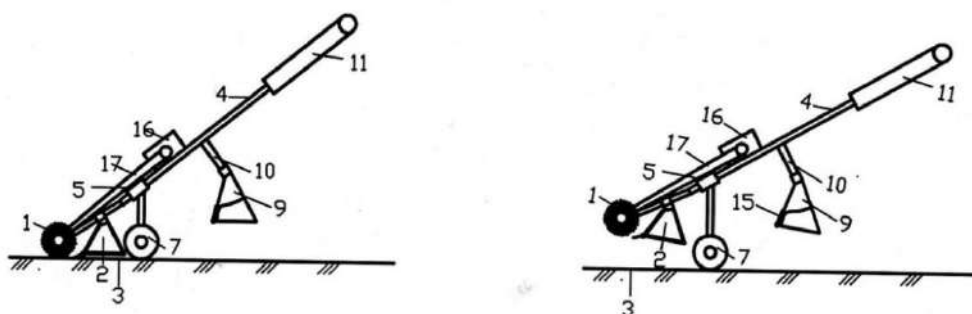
Рычажное барабанное устройство для подметания улиц и дорог: 1–барабанная щетка; 2 – призматический савок; 3– дорога ; 4 – черенок; 5 – патрубок; 6 – ось ОПМ; 7 – колеса; 8 – рама; 9 – компенсирующий призматический савок; 10 – кронштейн; 11 – рукоятка; 12 – винт; 13 – отверстие; 14 – упорный винт; 15 – откидной щиток; 16– двигатель; 17– привод.
